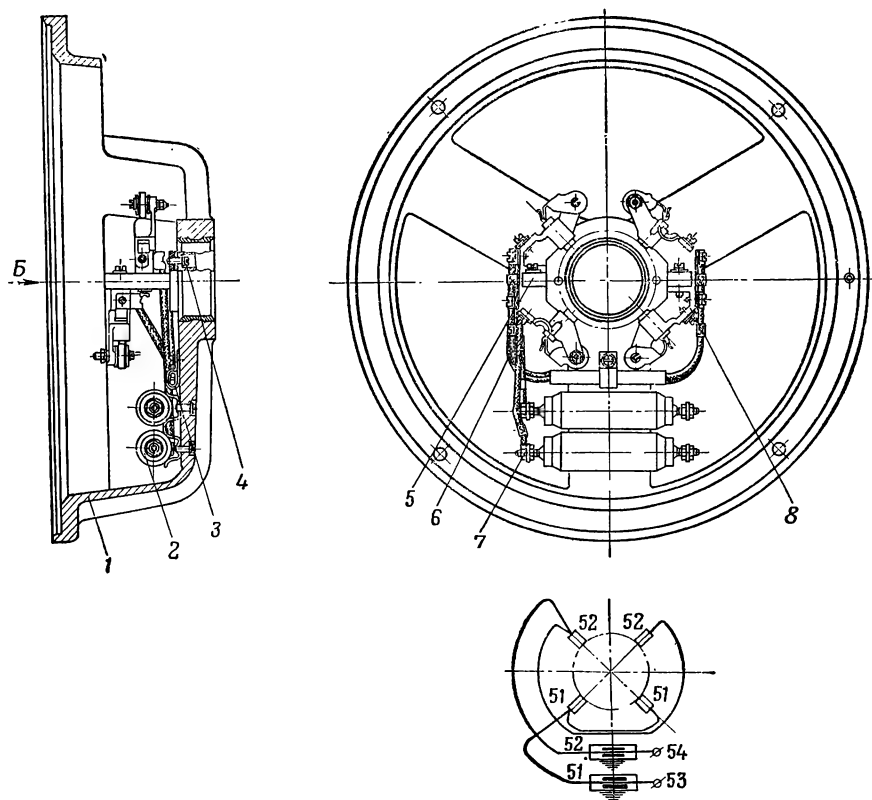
Подшипниковый щит генератора ГАБ-8-Т/230/Ч-400 со стороны контактных колец:
